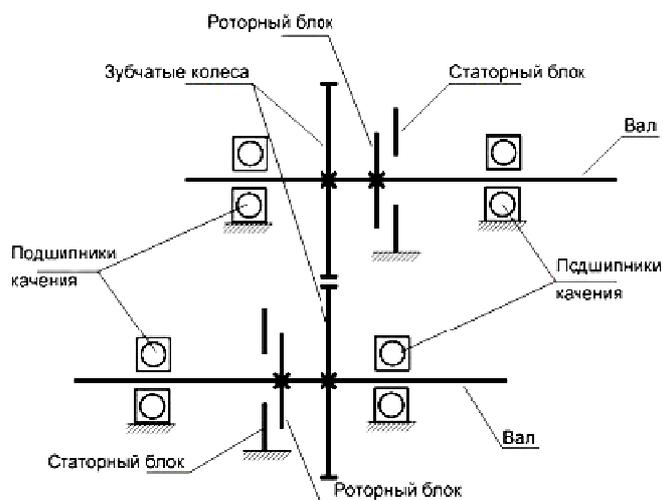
Кинематическая схема одноступенчатого зубчатого редуктора с устройствами измерения виброускорения
